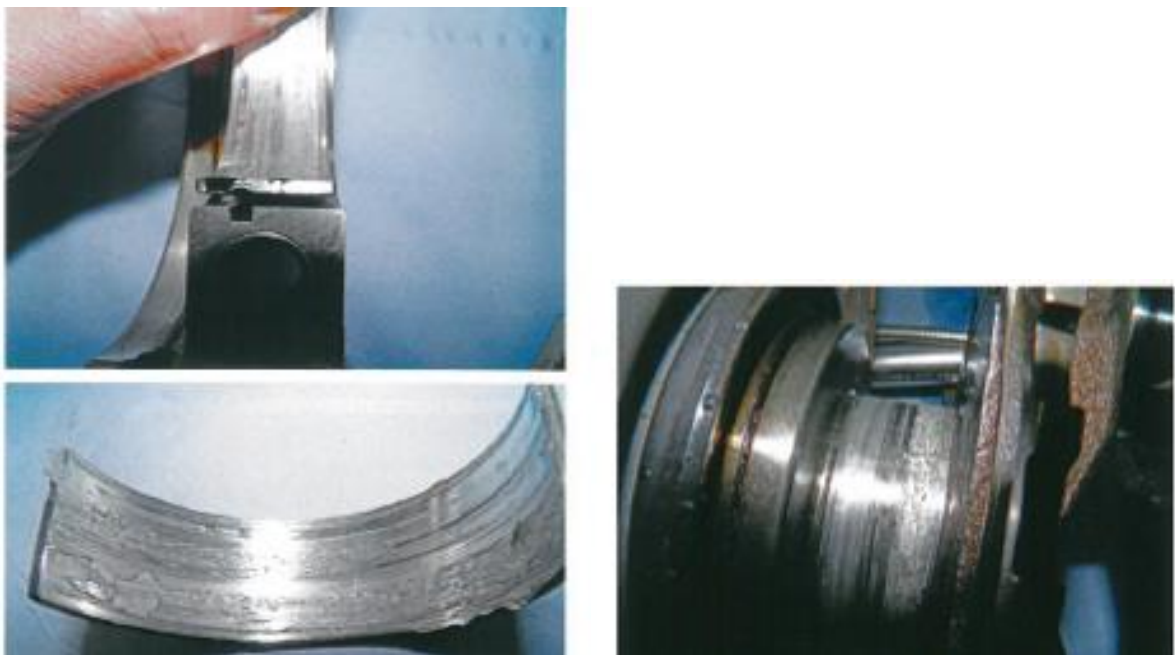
Повреждение заднего коренного подшипника – перегрев вкладышей, задиры на рабочей поверхности вкладышей и шейки коленвала произошло в результате производственного дефекта сборки (когда в нарушение сборочной технологии в двигателе был установлен бракованный блок цилиндров с уменьшенным диаметром отверстия коренного подшипника).
